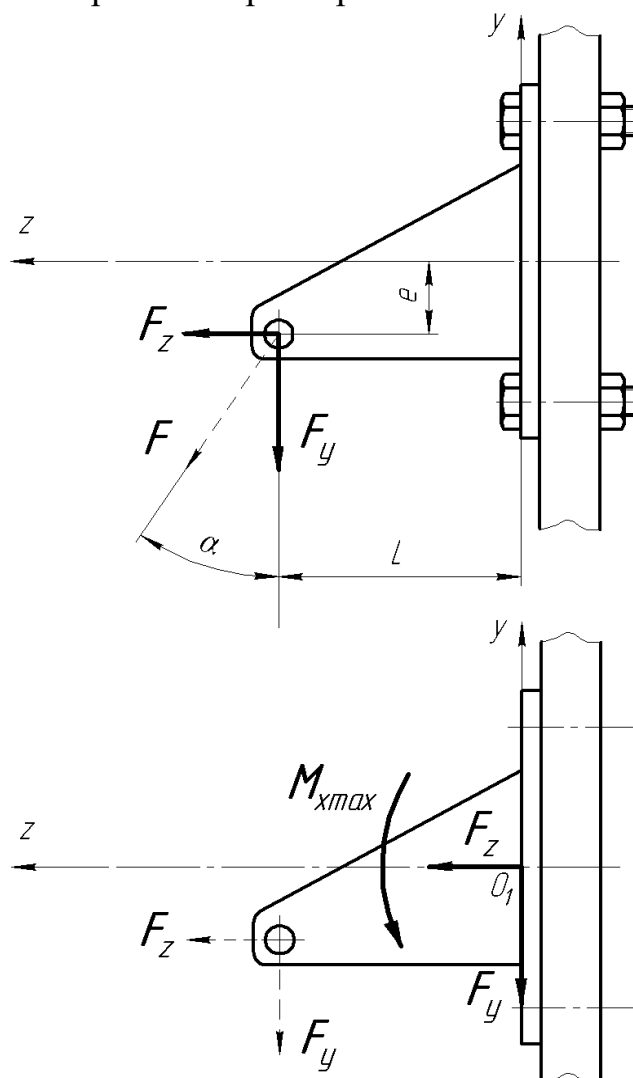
Разложение силы F на составляющие и перенос их в центр сварного шва.
